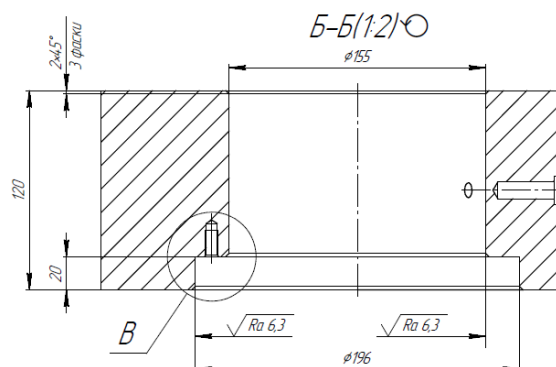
Вид з креслення деталі «Фланець»
